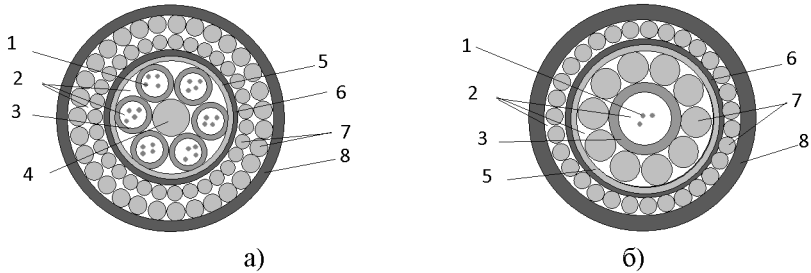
Конструкції кабелів із двошаровою бронєю для прокладки в ґрунт:
